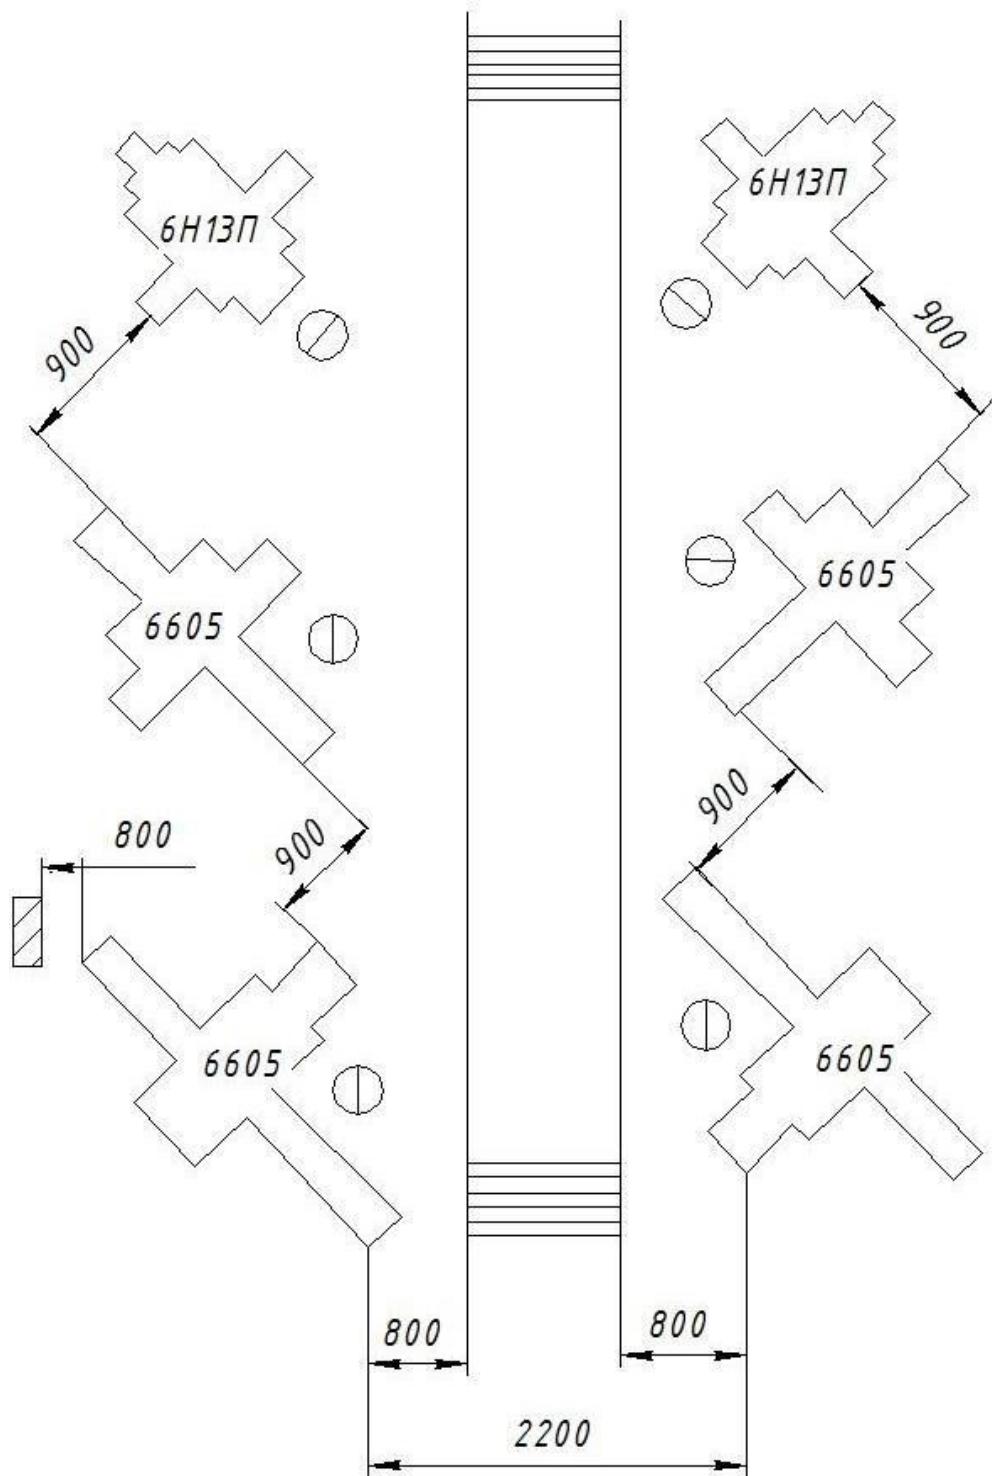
Паніровка ділянки механічної обробки консолі
